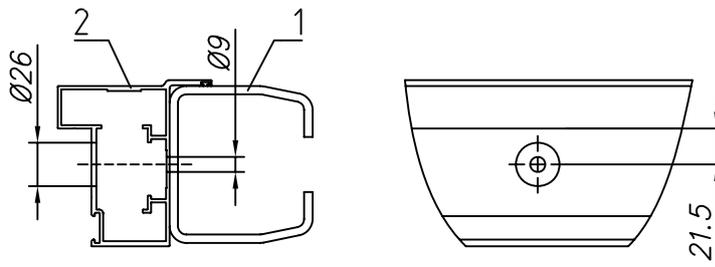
Размеры и расположение отверстий для крепления балки нижней и шины
